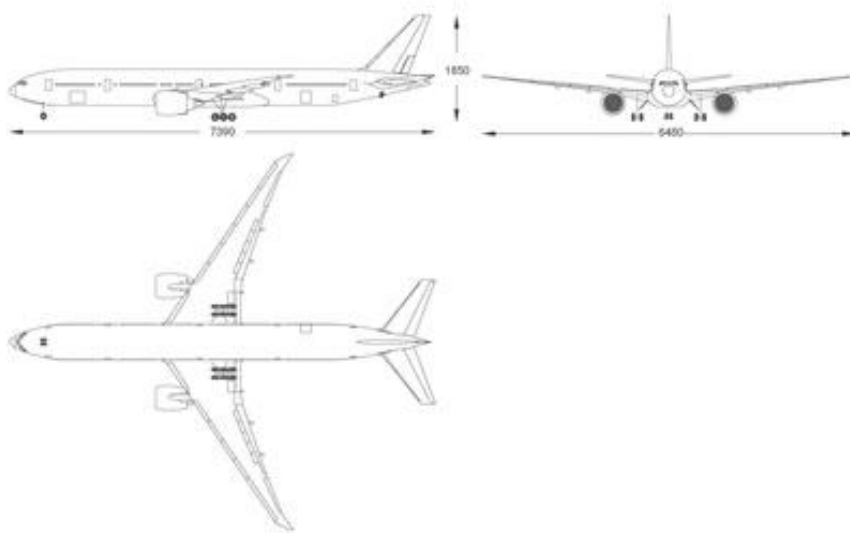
Загальний вигляд Boeing 777-300ER
